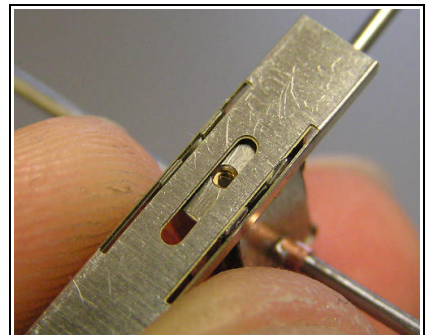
Die Achse soll so in dem Chassisblech passen. Die Position ist in der Länge (Achsabstand) einstellbar.
